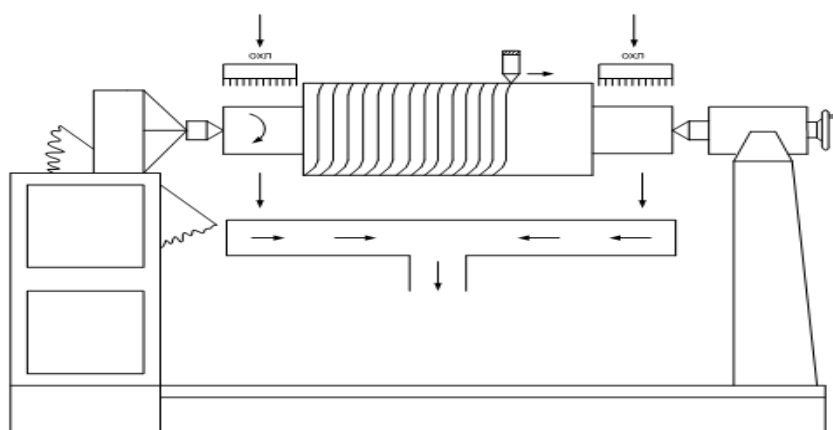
Схема наплавки с принудительным охлаждением шеек вала
